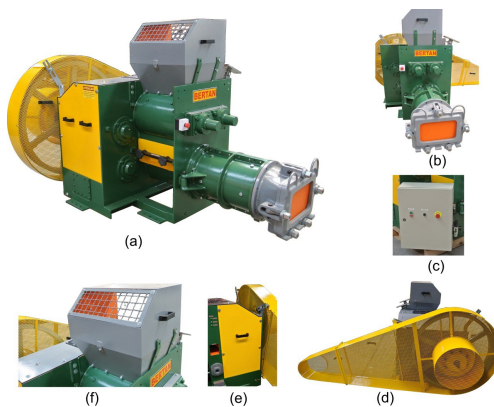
Extrusora à Vácuo: a - Extrusora à Vácuo E.B 250 Adequada, b - Botão de Emergência, c - Painel Elétrico, d - Proteção da Transmissão de Potência, e - Caixa de Engrenagem, f - Proteção Capota.
